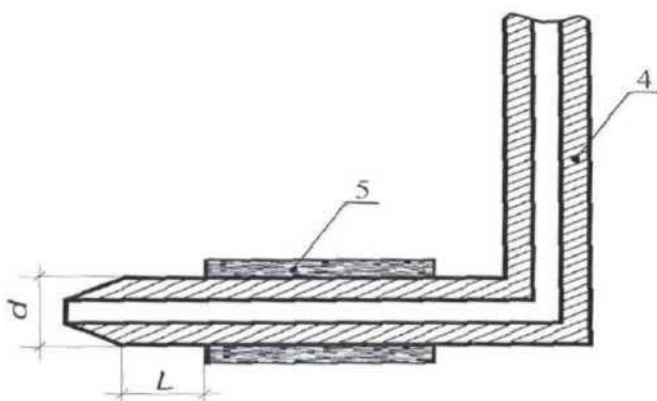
Схема розташування напиленого термоперетворювача опору
